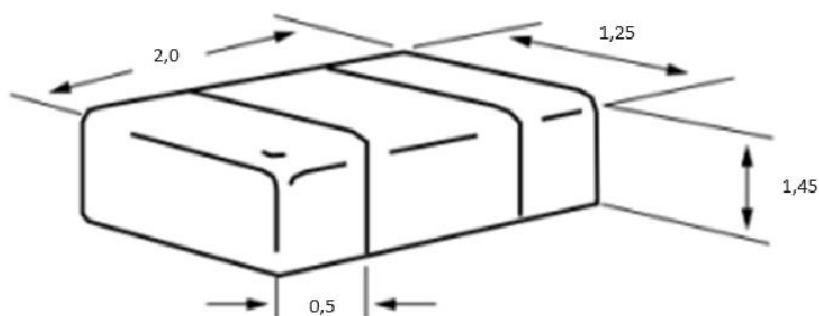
Зовнішній вигляд та габаритні розміри конденсатора в корпусі SMD0805
